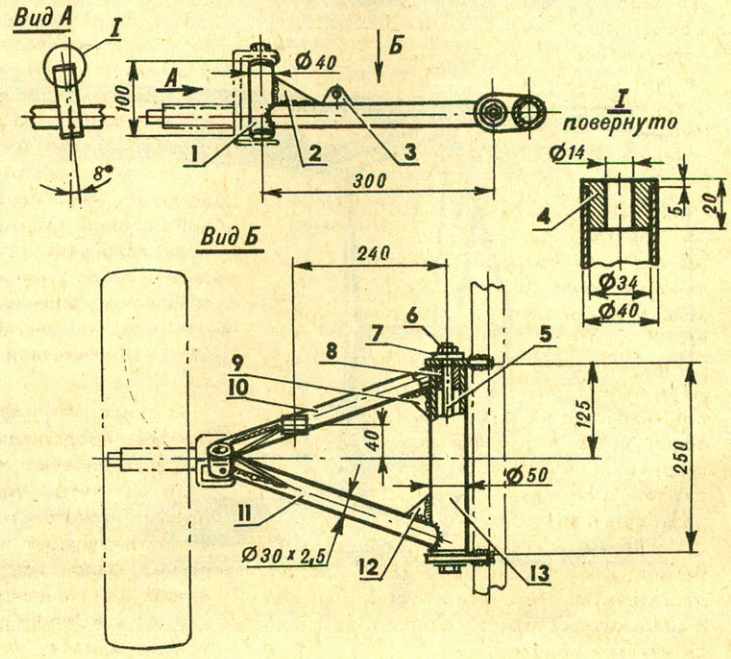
Рычаг подвески передних колес: 1 — шарнир поворотной вилки колеса, 2 — косынка, 3 — кронштейн-вилка амортизатора подвески, 4 — бронзовая втулка, 5 — ось качалки, 6 — гайка оси подвески, 7 — шайба, 8 — бронзовая втулка, 9 — косынка, 10 — передняя труба рычага, 11 — задняя труба рычага, 12 — косынка, 13 — корпус рычага.
